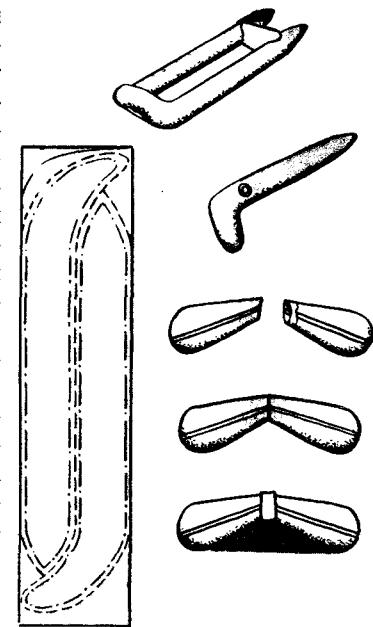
Схема сборки лодки комбинированным способом, борта которой изготовлены из невулканизированных материалов.
